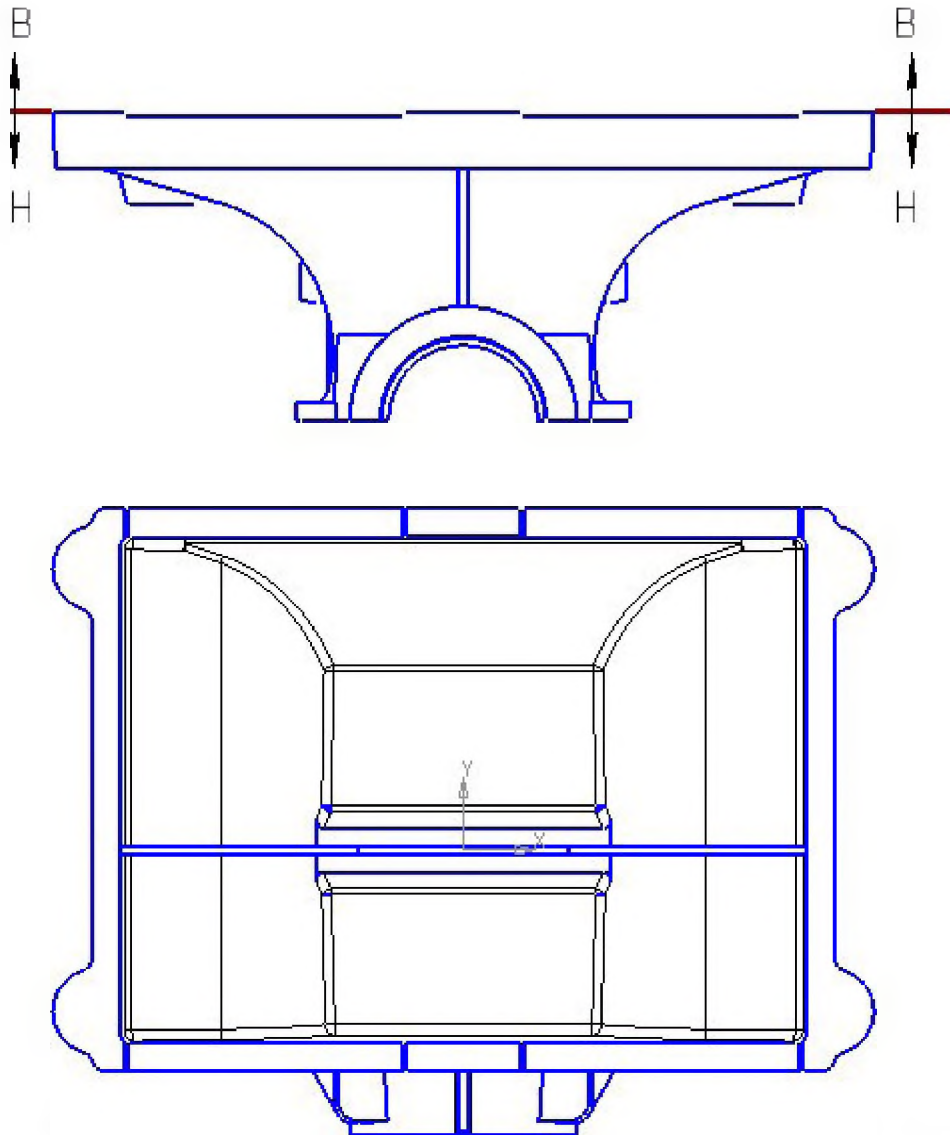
Ескіз заготовки деталі «Корпус»
